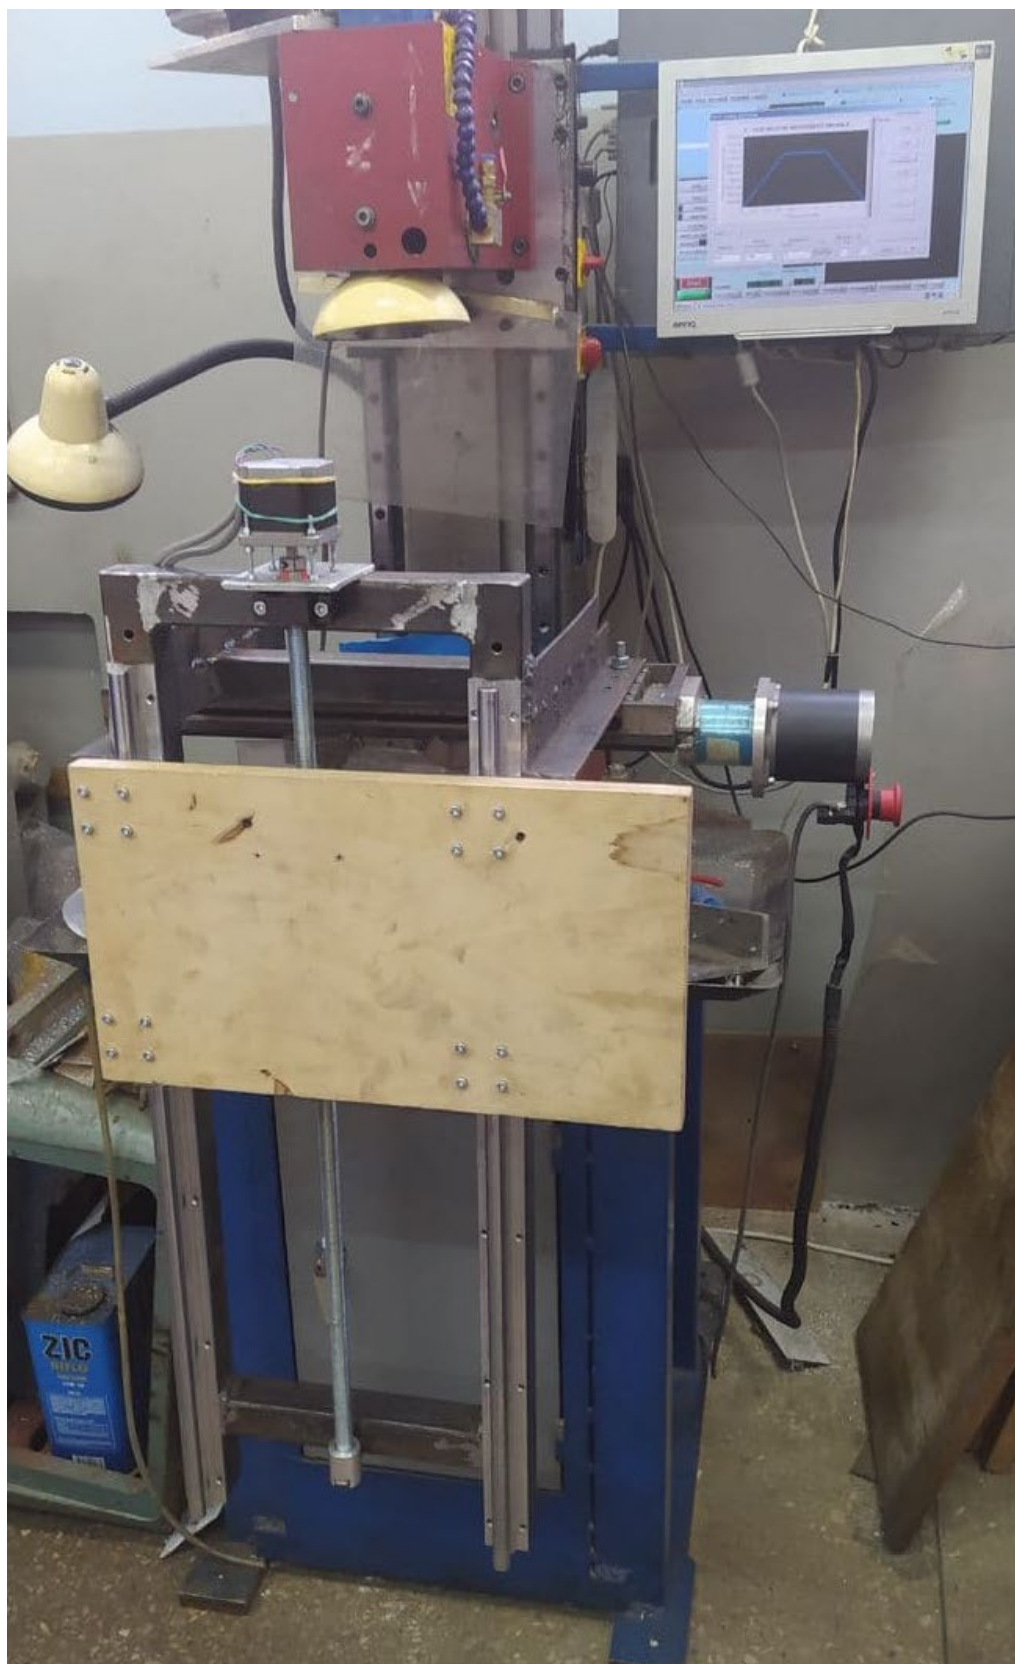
Розроблена конструкція на верстаті з ЧПК
